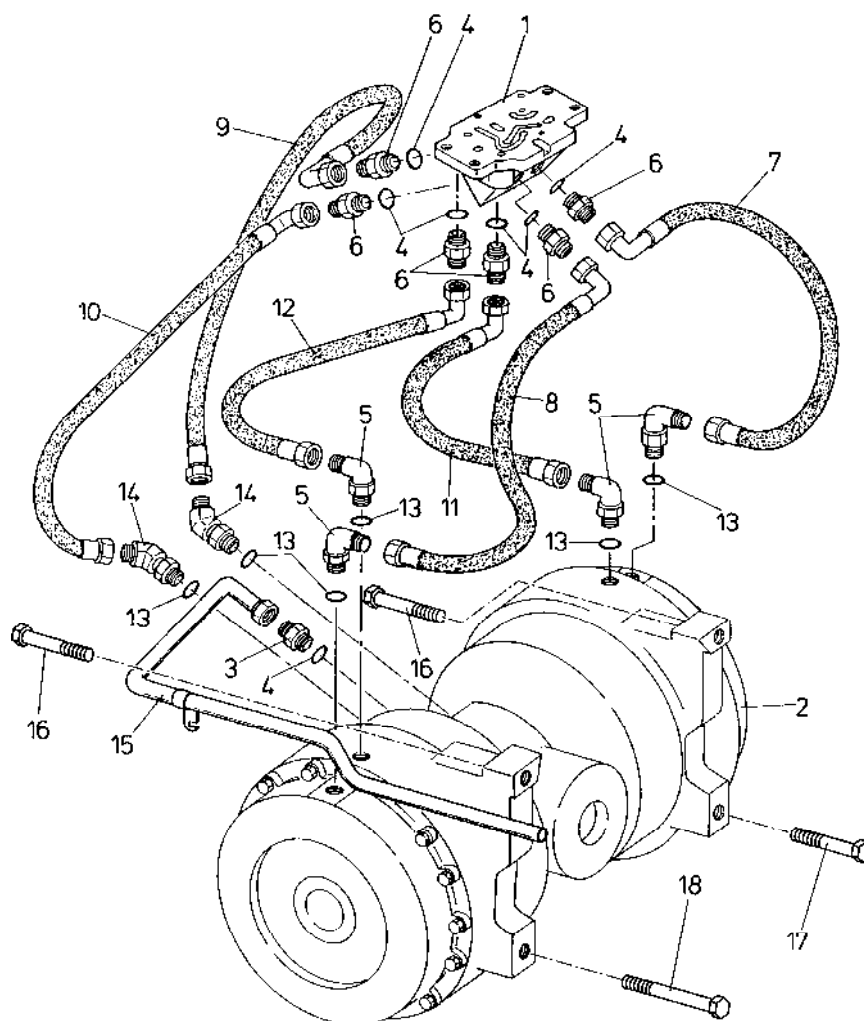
Е.7. Двухскоростной механизм поворота со шлангами
